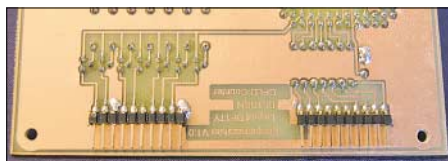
Unter die Hauptplatine werden abgewinkelte Steckerleisten gelötet.
